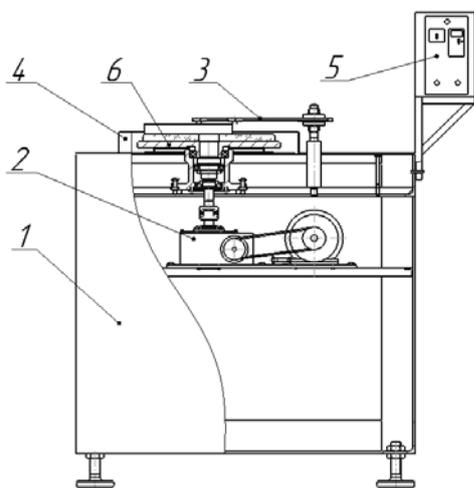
Схема установки для абразивной обработки карбидокремниевых пластин
